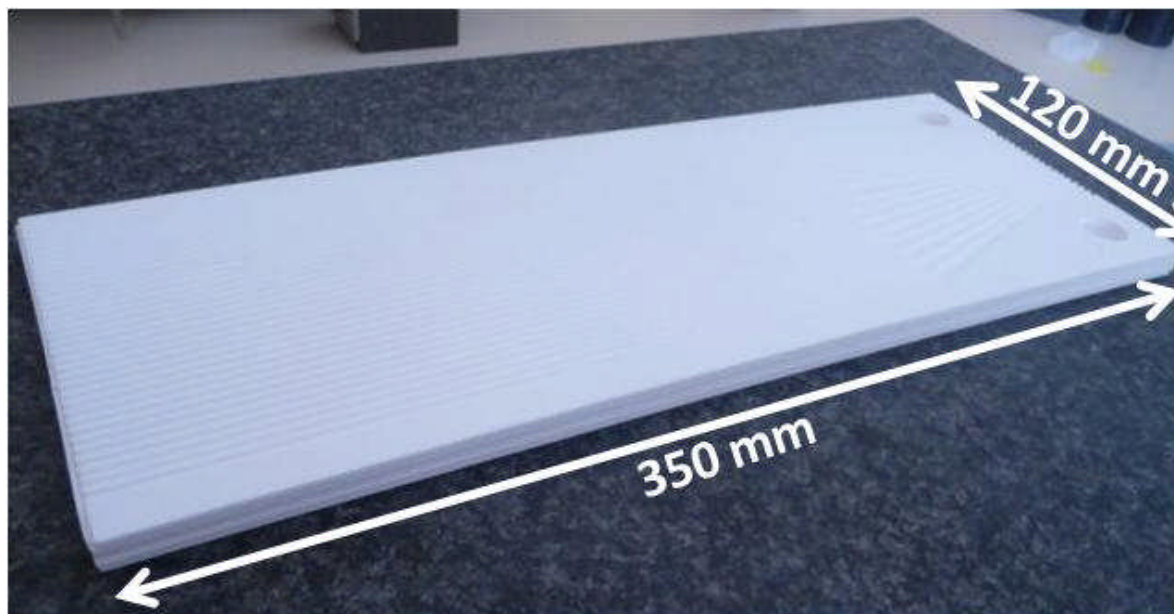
Résultat d'assemblage d'un module de 5 plaques taille ETR.
